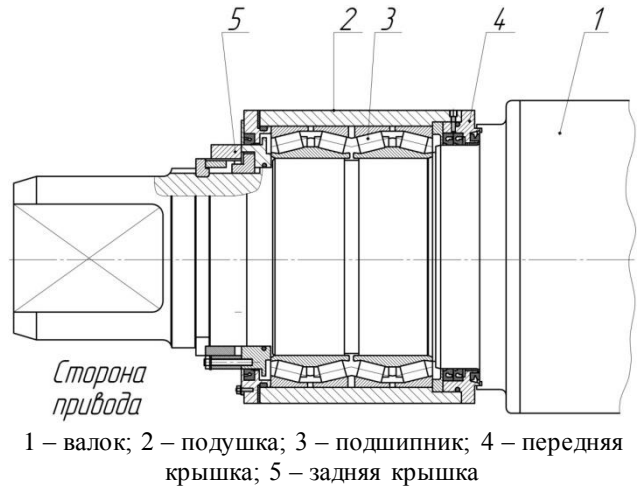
Опора рабочего валка клетки чистовой группы НШС-1700
